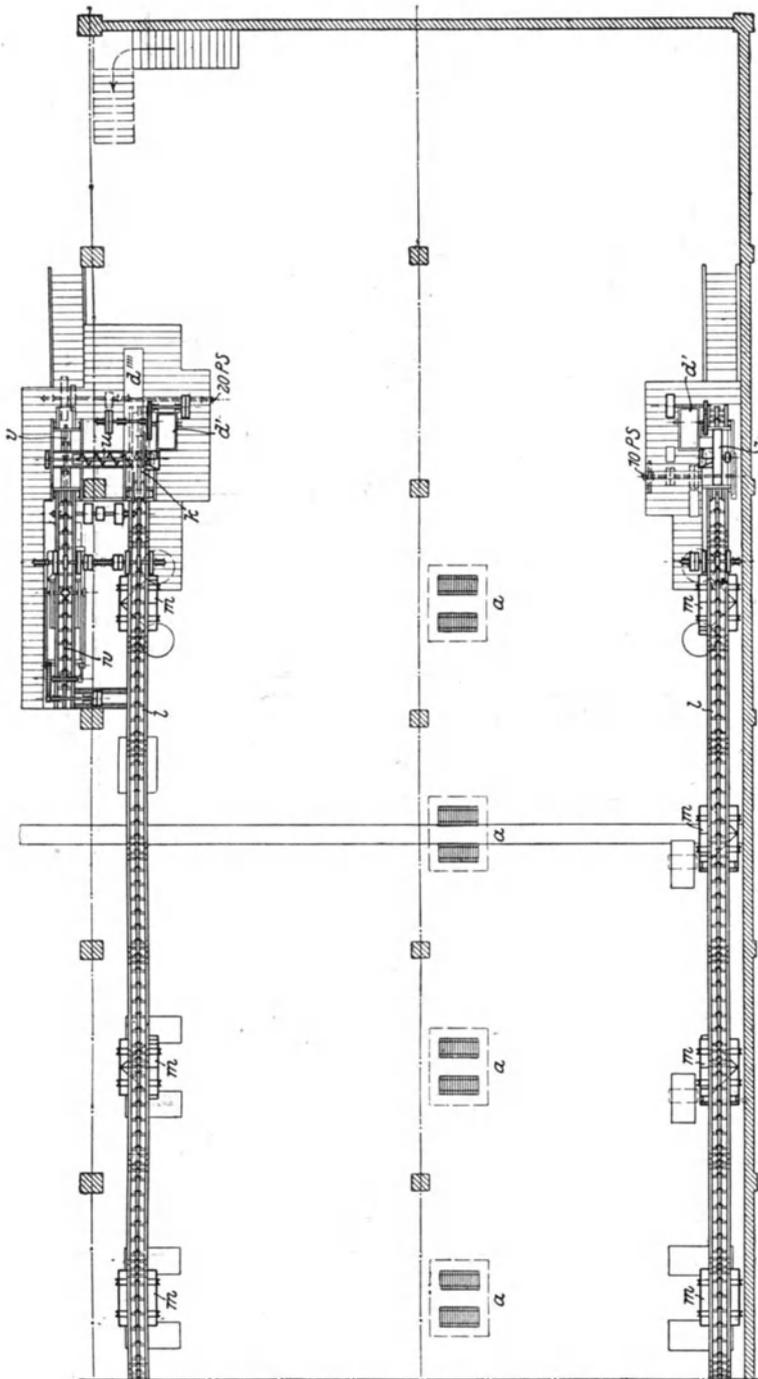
b. Sandaufbereitungs- und Förderanlage. Grundriß des Erdgeschosses.
